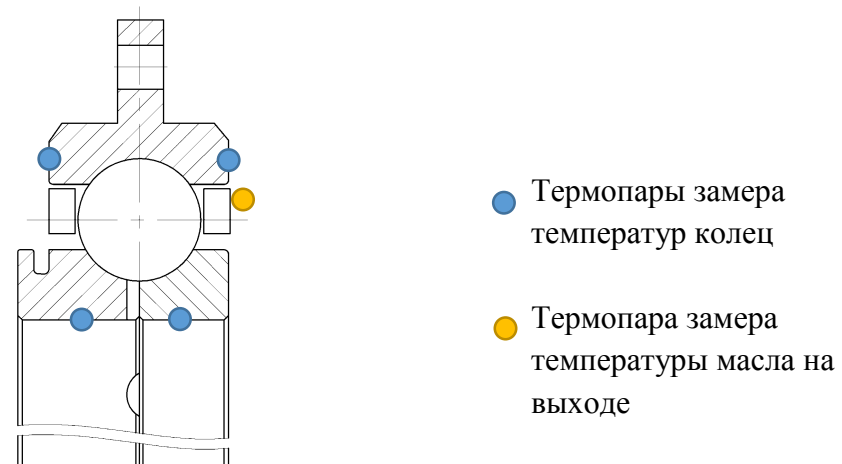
Схема препарировки колец подшипника термопарами
